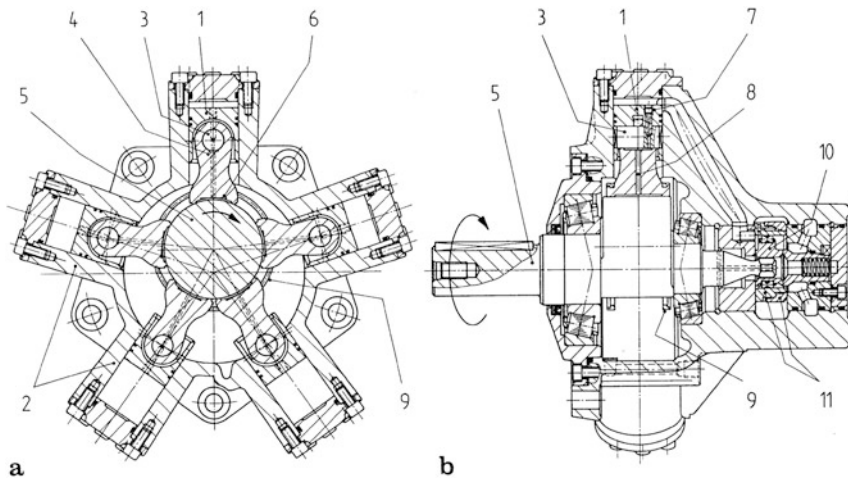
Radialkolbenmotor, innen abgestützt, in der Variante „Schubkurbel“ (RM, Düsterloh). a Querschnitt; b Längsschnitt
